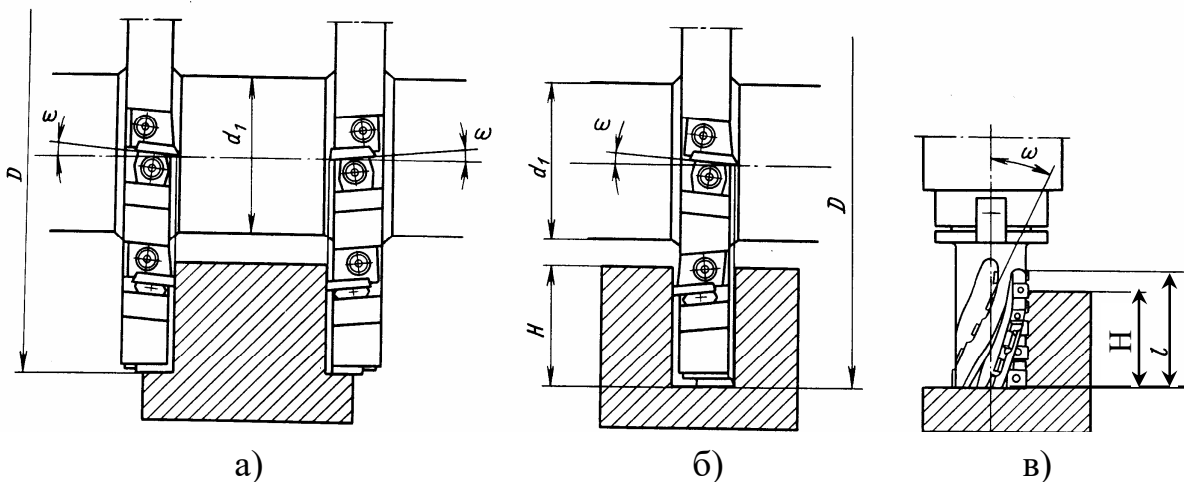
Схеми фрезерування: а – виступів набором двосторонніх фрез; б – паза тристоронньою дисковою фрезою; в – уступу кінцевою фрезою
